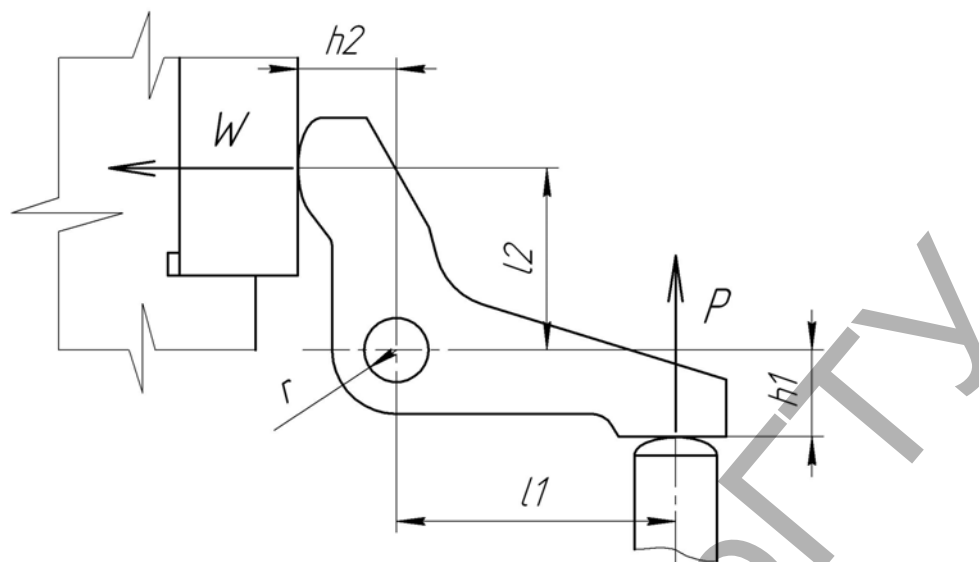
Двухплечевой угловой рычажный зажимной механизм
